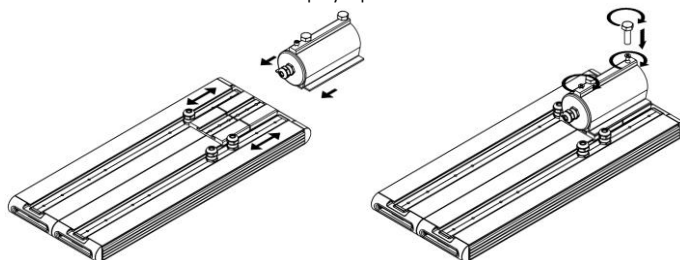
Установка крепления на соединительные планки на примере светильника Element 0,5x2 и Крепления Консоль без регулировки.
